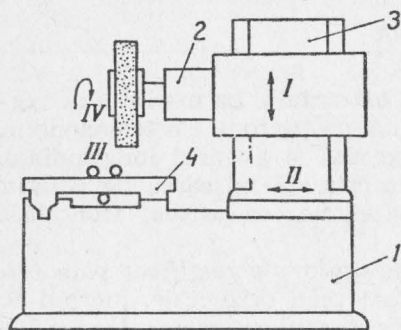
Mașina de rectificat plan orizontal cu coloană deplasabilă transversal:
